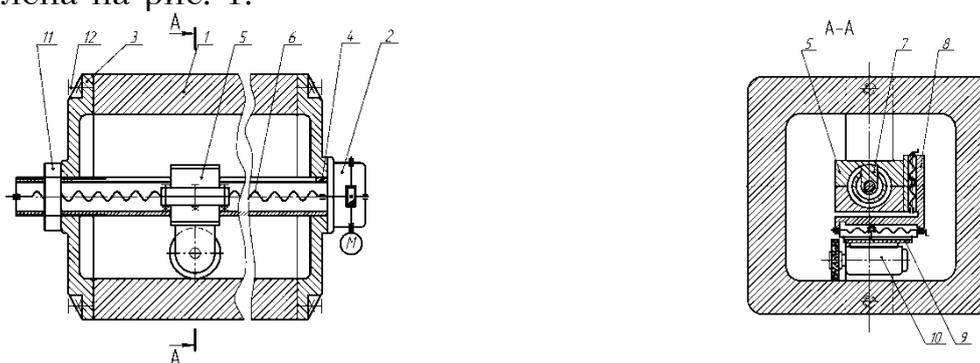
Схема установки: 1 – изложница, 2 – червячный редуктор, 3 – траверса, 4 – цилиндрическая направляющая, 5 – ползун, 6 – винт, 7 – гайка, 8 – механизм прижима шлифовального круга, 9 – механизм поперечного перемещения шлифовального круга, 10 – шлифовальная головка, 11 – гайка крепления направляющей, 12 – винты крепления траверсы.
